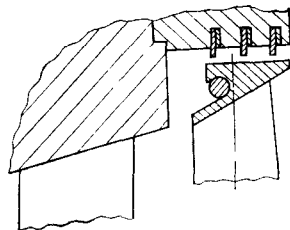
Целнофрезерованный бандаж с расположенной в нем демпферной проволокой
